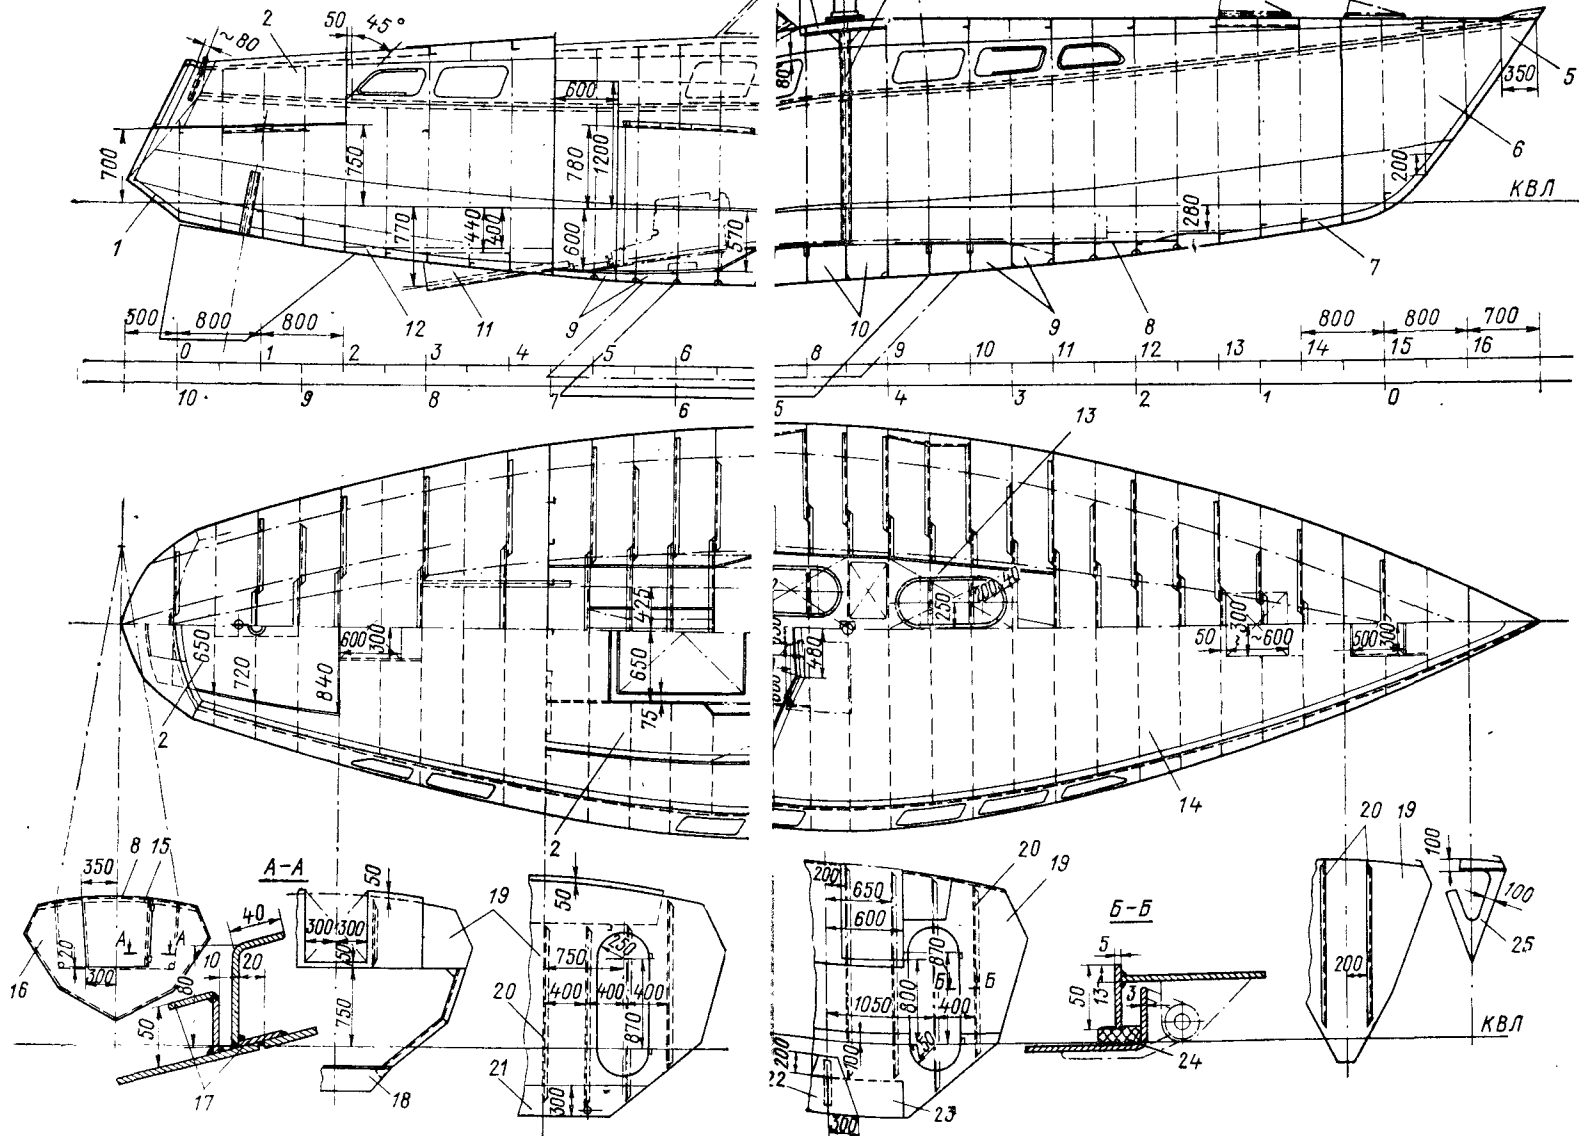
Конструктивный чертеж корпуса 14-метровой яхты «Гидра».
